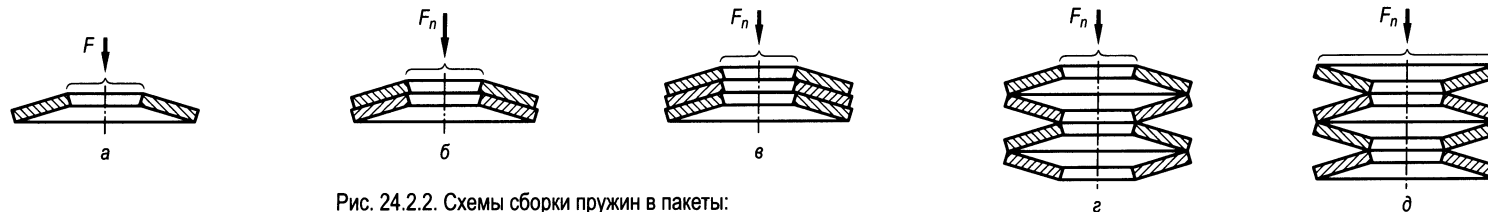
Схемы сборки пружин в пакеты:
